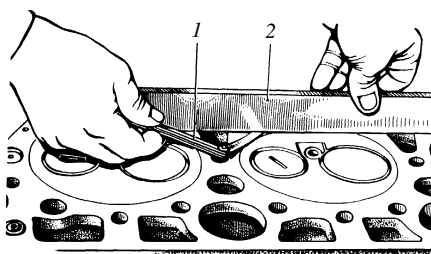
Проверка коробления плоскости головки цилиндров: 1 – щуп; 2 – поверочная линейка
